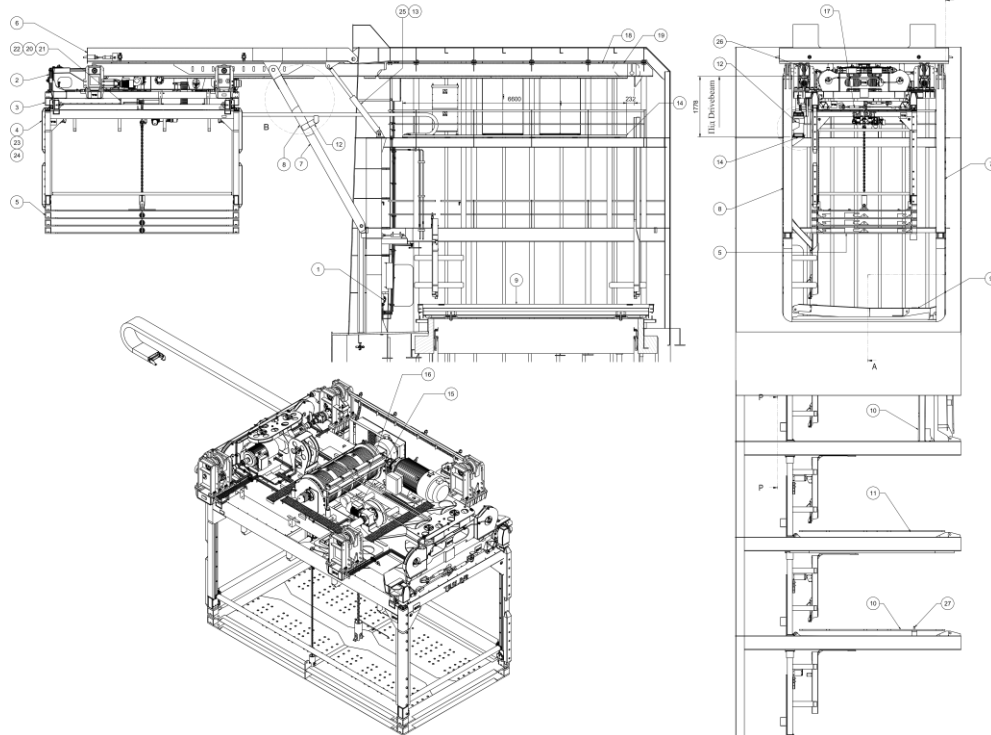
Вантажно-розвантажувальна система палетів рефрижераторного судна: 1 – установка гідравлічна; 2 – металева змонтована конструкція візка; 3 – металева змонтована конструкція розподільника; 4 – клітка; 5 – додаткова нижня пластина; 6-8 – бокові двері; 9 – кришка люка верхньої палуби; 10 – кришка люка другої/четвертої палуби; 11 – кришка люка третьої палуби; 12 – кабель мережі підтримки лівосторонньої збірки; 13 – кронштейн циліндра на палубі; 14 – лоток для кабельного ланцюга; 15, 16 – трос; 17 – фаркоп; 18, 19 – лівий та правий привід візка, відповідно; 20 – живлячий кабель; 21 – кронштейн кріплення кабелю; 22 – кабельні хомути; 23 – надпотужний роз'єм; 24 – кабельний ввід; 25 – гідравлічний циліндр; 26 – упор для датчика; 27 – вісь; 28 – пластина блокування внутрішньої позиції візка; 29-31 – шайба кріплення приводу Drivebeam; 32 – шайба; 33 – шестигранна самоконтр. гайка; 34 – гвинт головки блоку циліндрів.
